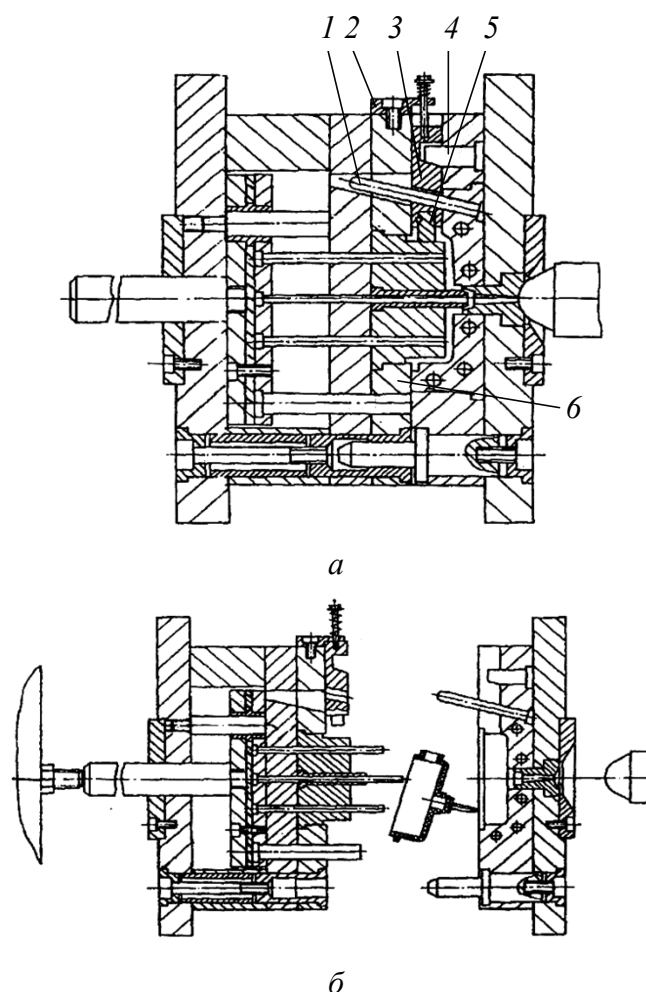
Литьевая форма с отверстием на боковой поверхности изделия
